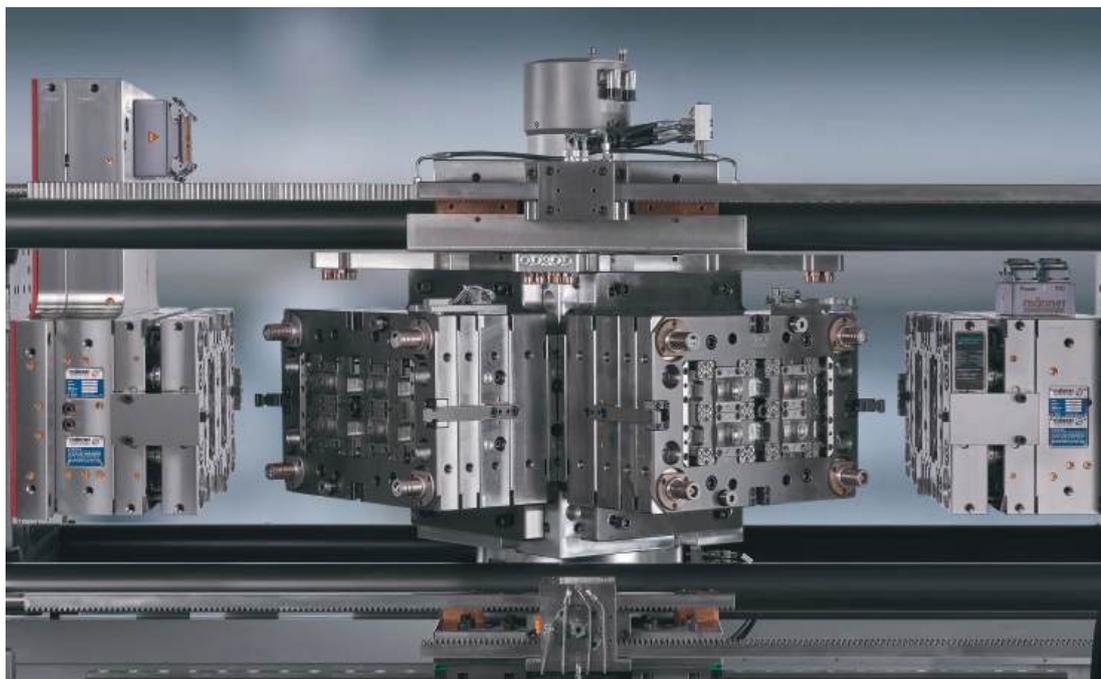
Der Compact-cube ist für die Automobil- und Elektronikindustrie sowie die Medizintechnik attraktiv.
